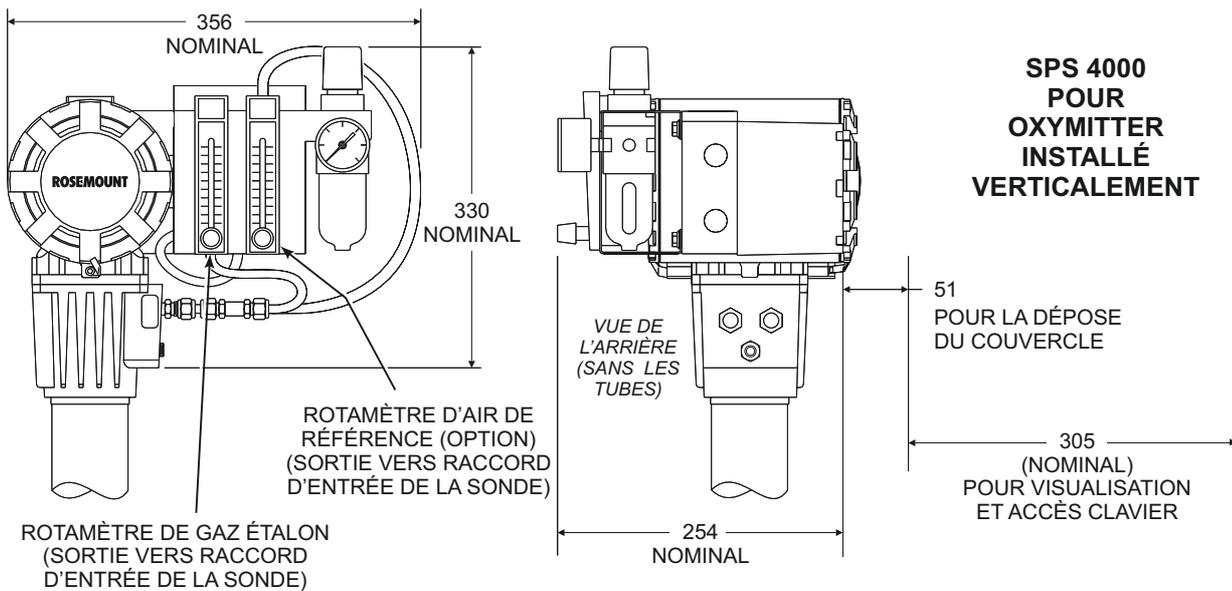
Dimensions et tuyautage des SPS 4000 intégrés
